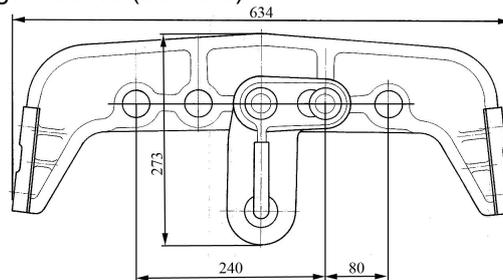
Schéma d'installation du dispositif TSU-1J
